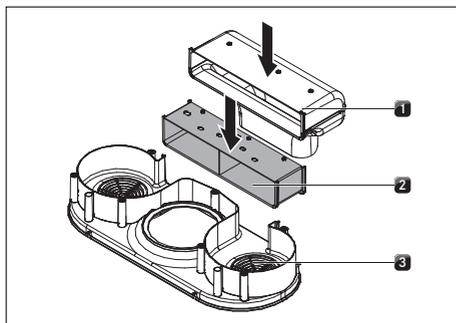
Mise en place du prolongement du conduit d'évacuation d'air
